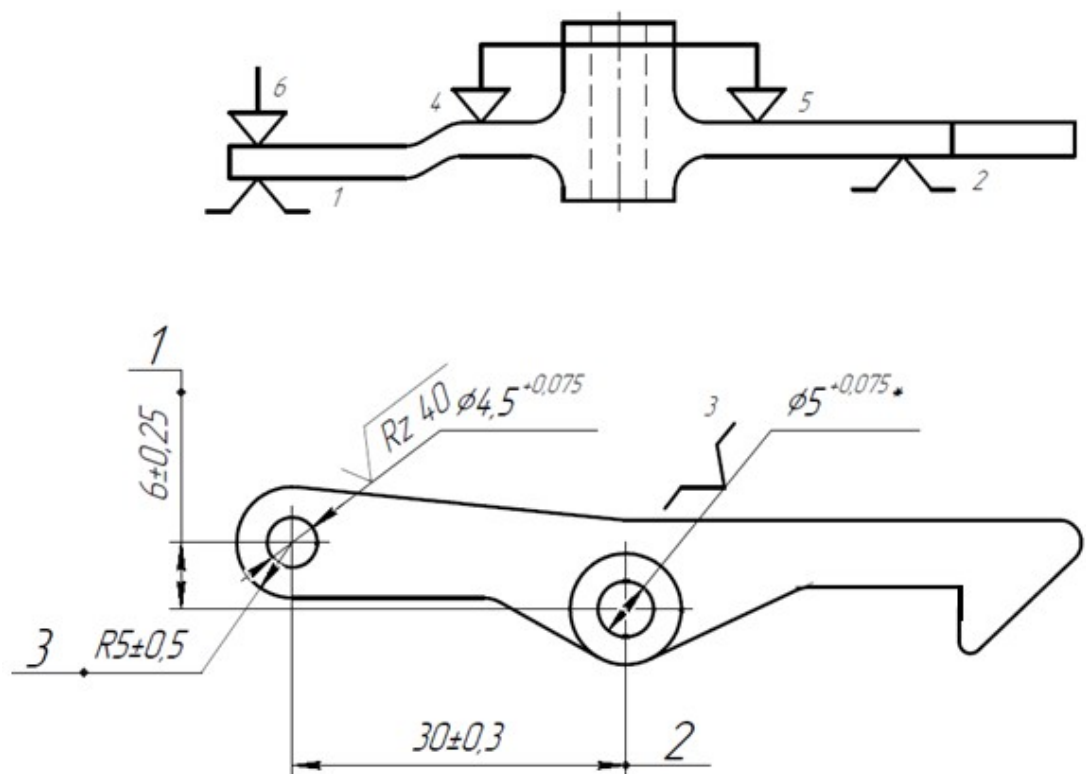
Ескіз базування п'ятої механічної операції, свердлильної.
